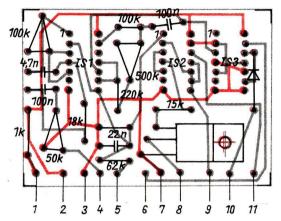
Bestückungsplan Platte 1 (Anschlußpunkte nach Tabelle 1)
